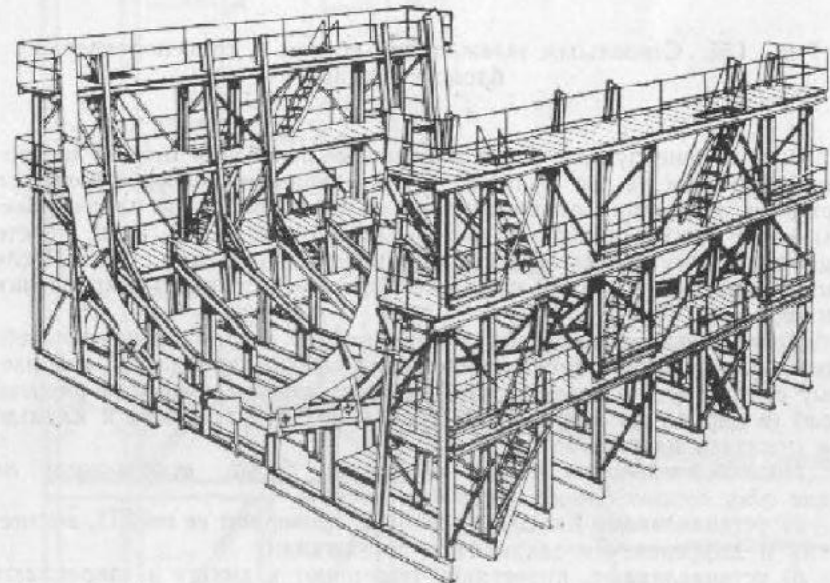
Станель-кондуктор для сборки и сварки блоков секций.
